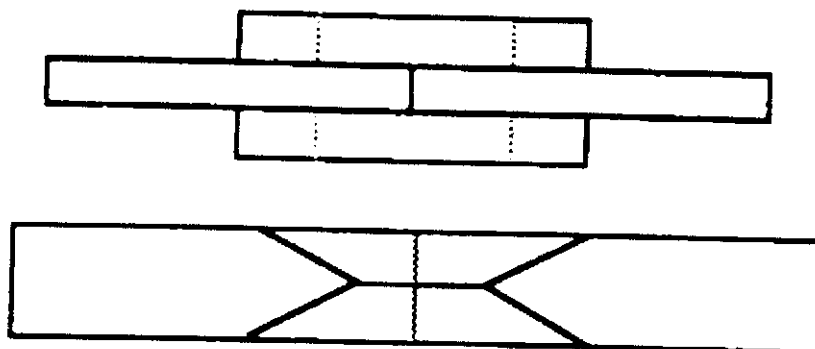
Diseño de soldadura a tope reforzada (178)
